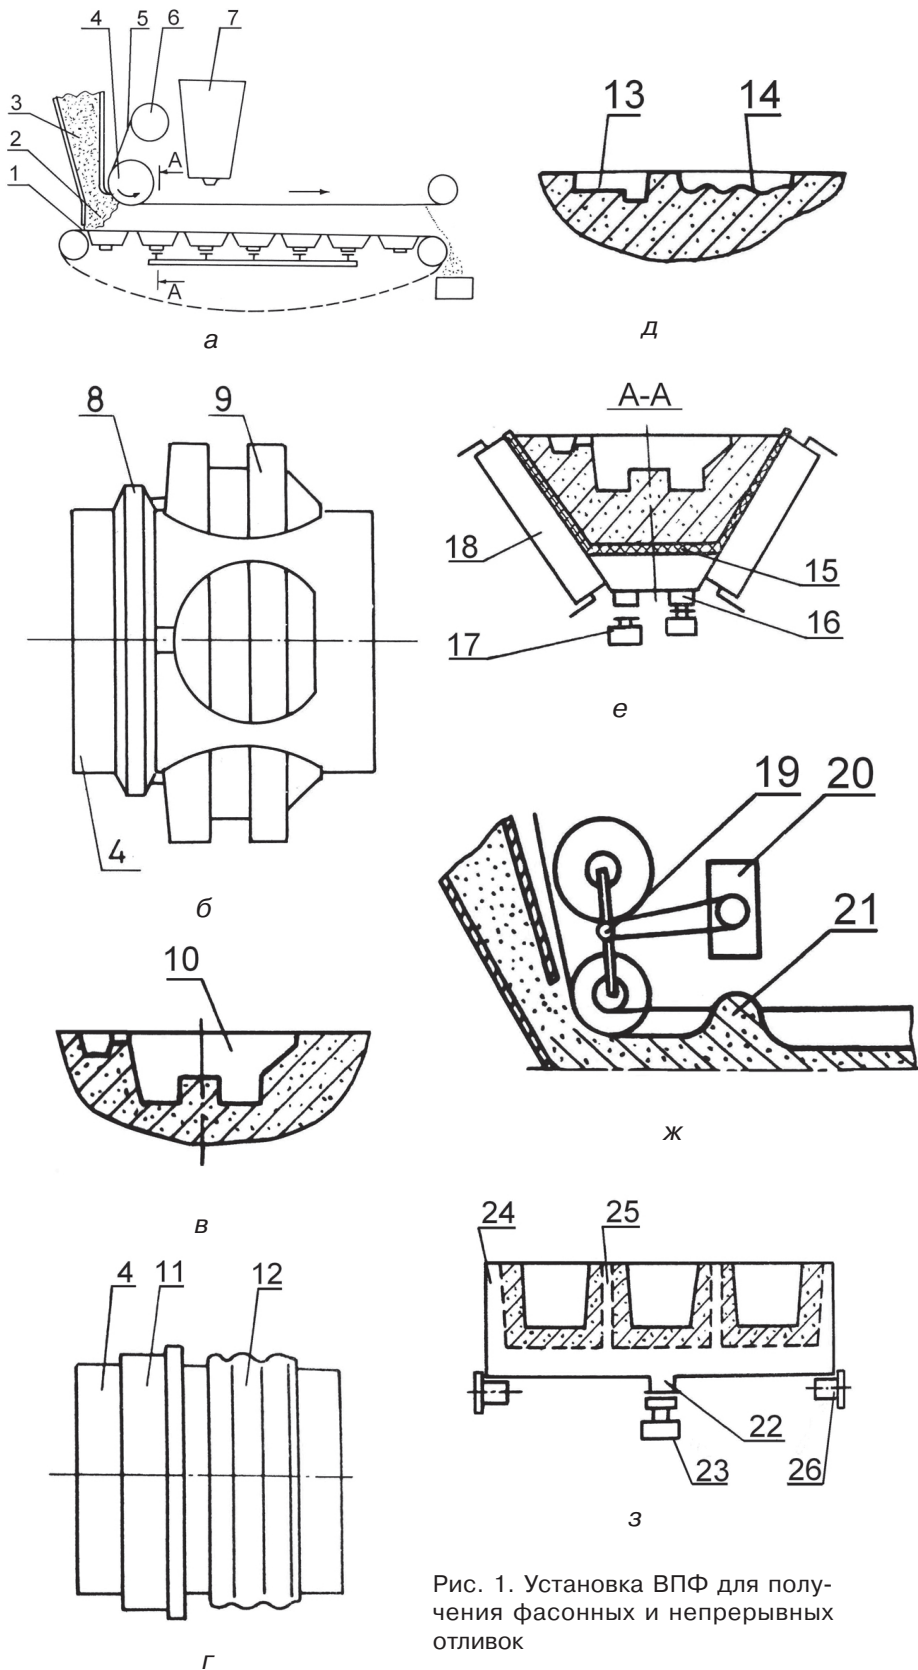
Установка ВПФ для получения фасонных и непрерывных отливок
